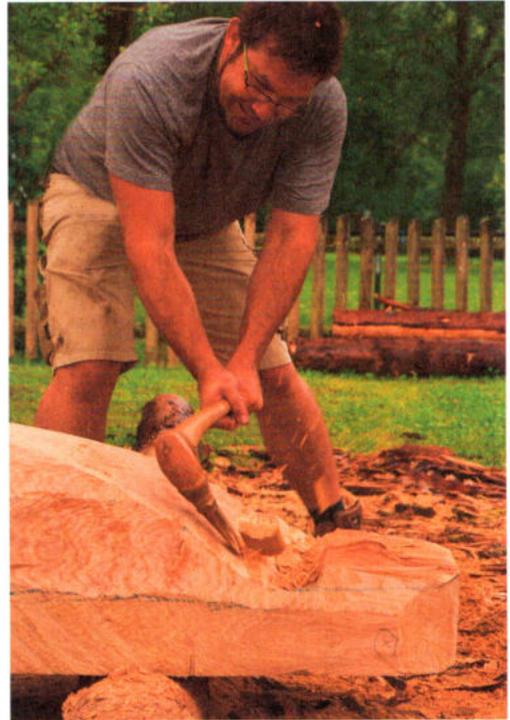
Um den Bug zu gestalten, setzten wir unser Tüllenbeil ein. – To form the upper end of the log boat we used our socketed axe.
